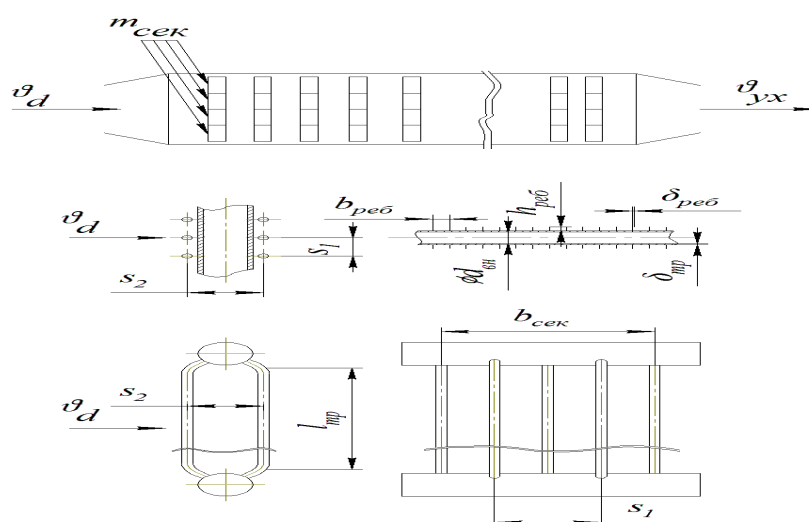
Конструктивные параметры типовой секции поверхностей нагрева КУ
